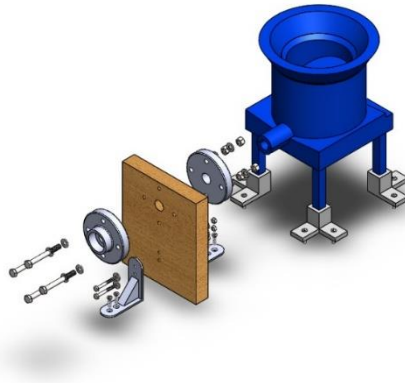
Montaje explosionado madera de aislamiento. Fuente: Propia.
